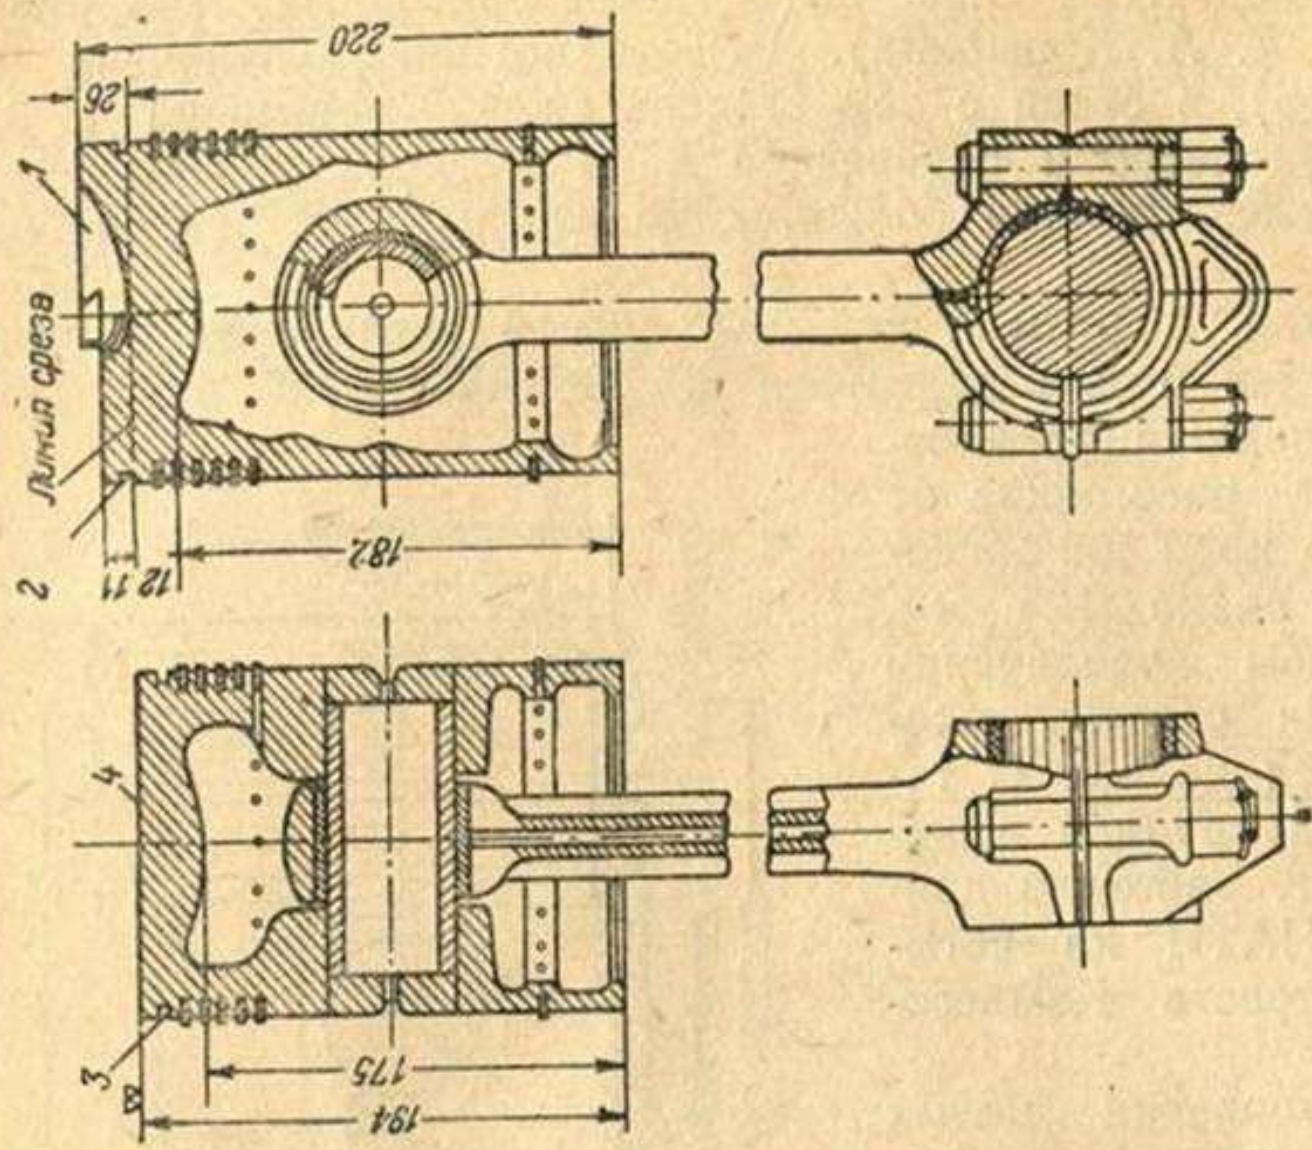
Поршни двигателя М-17 — газовый (слева) и дизельный (справа):
